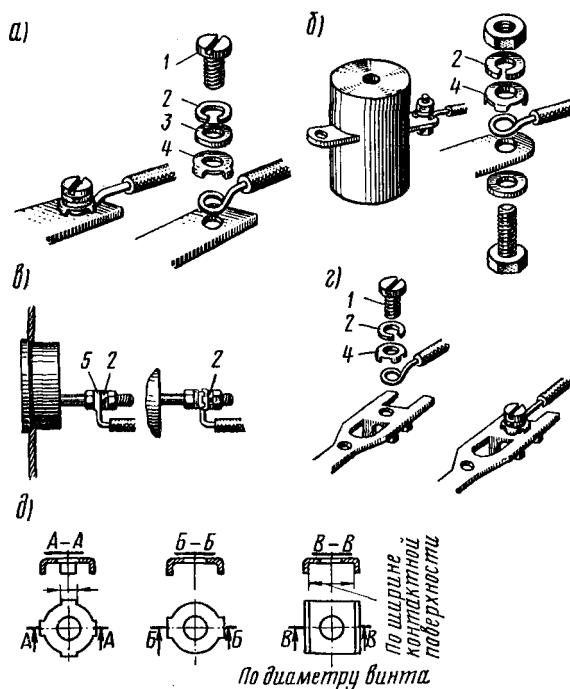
Схемы присоединения (а — д) алюминиевых жил:
